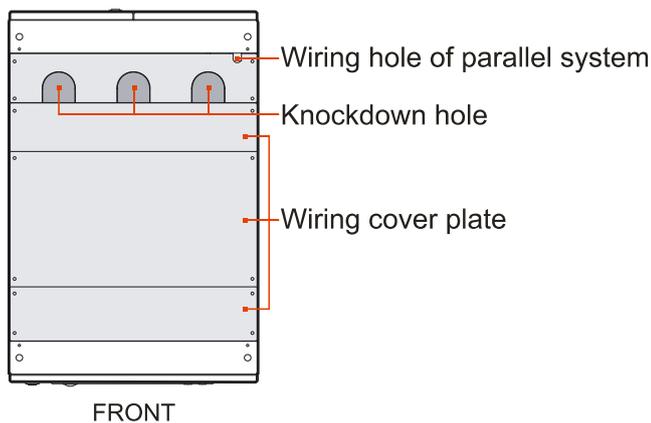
Верхняя монтажная крышка (вид сверху)
